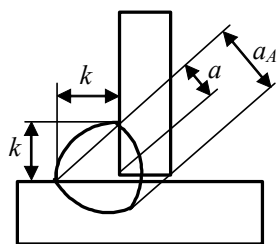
Переріз однопрохідного шва при зварюванні під флюсом
